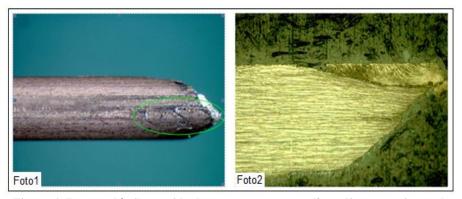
Fratura dúctil ocorrida durante o teste com a 1ª condição experimental.
